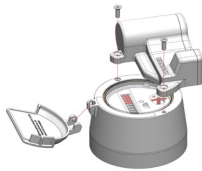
Montage des EDC-S auf Zähler mit Kupfer/Glas-Zählwerk (IP68)
